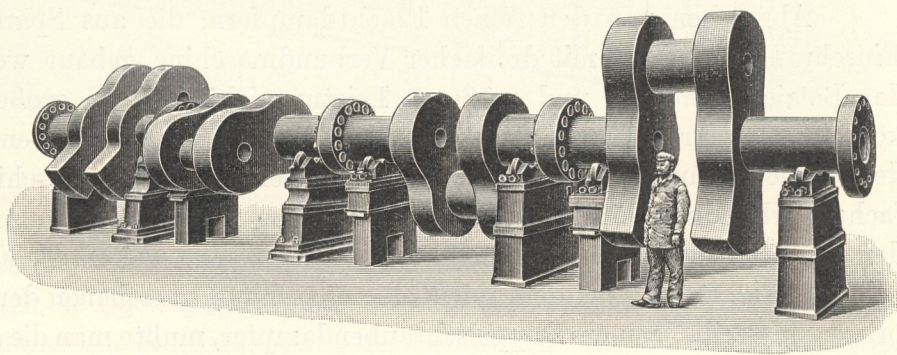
Vierfache Kurbelwelle des Schnelldampfers „Kaiser Wilhelm der Große“.
